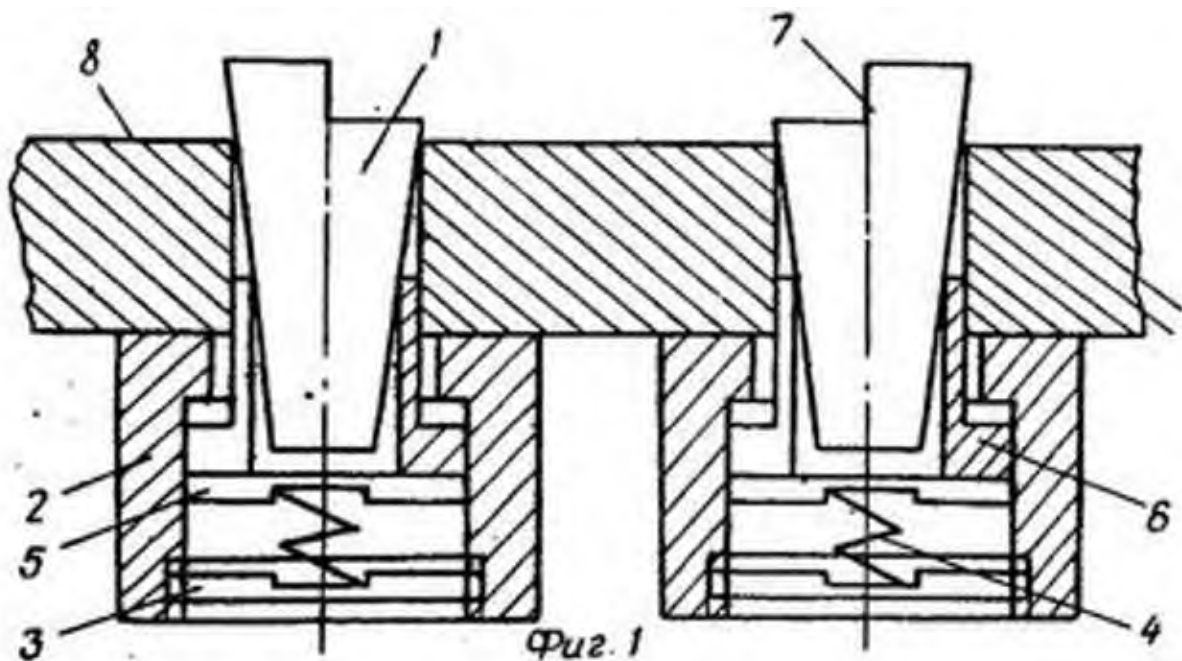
Схема пристрою з свідоцтва №1634978
